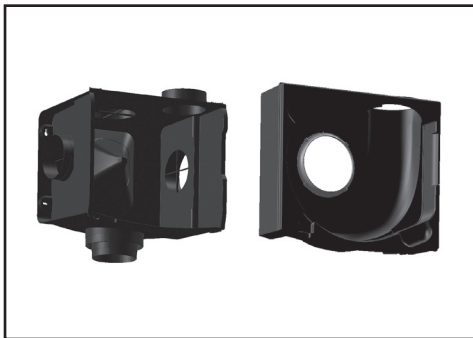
Anschlusskasten mit Spiralgehäuse und Einlassring
